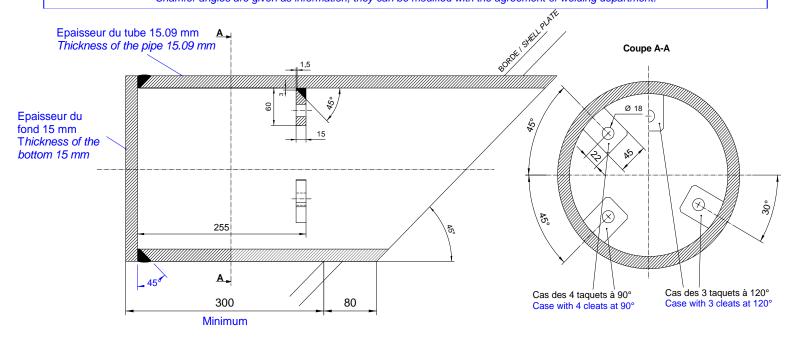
DETAIL DU MANCHON / DETAILS OF SPOOL PIECE
